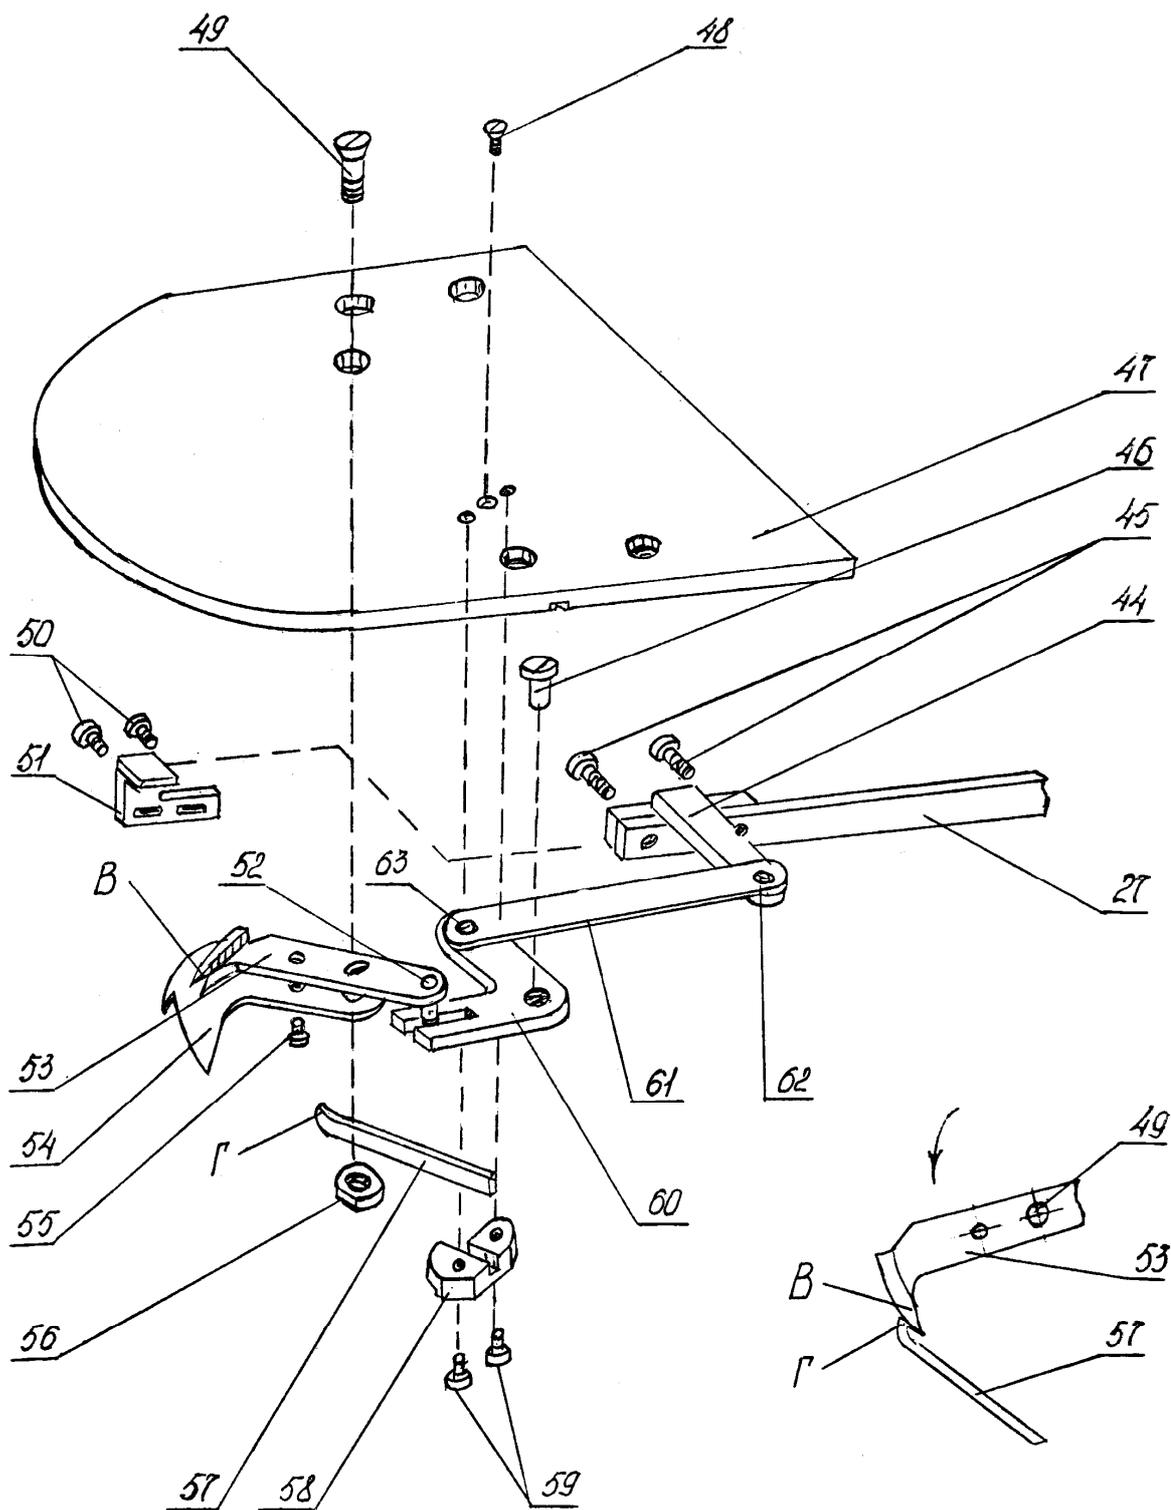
Механизм обрезки нитей. Ножевое устройство
